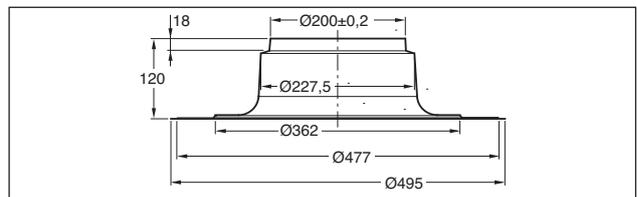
Flachdach-Klebeflansch (Maße in mm)
